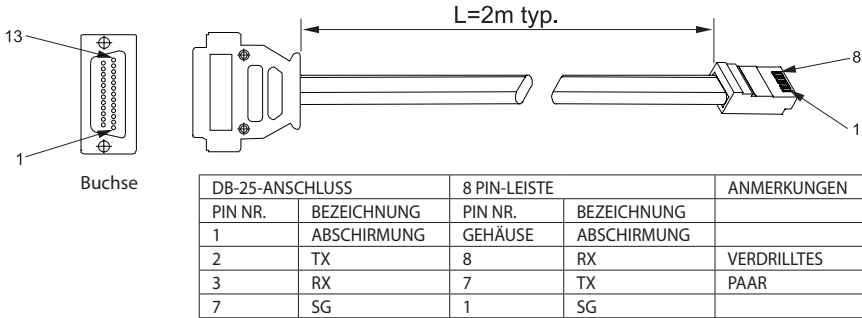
RS232- Kabel mit DB25 Anschlussstecker (P/N: Z/232-25)
